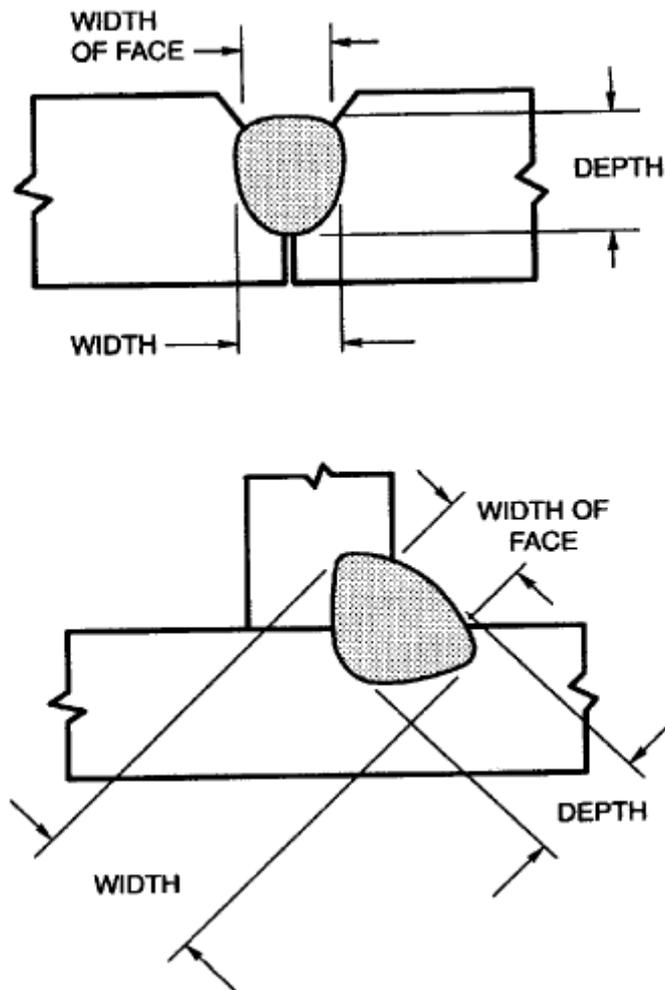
Ancho y profundidad de gota soldada que excede la cara de soldadura.
